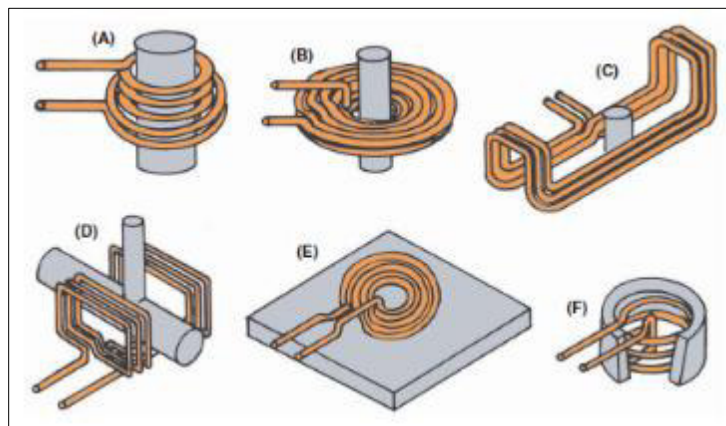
Esquemas de diseños básicos de bobinas de inducción para soldar tubería de cobre.
